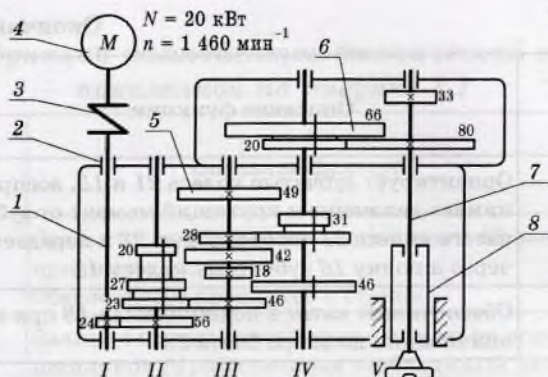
Кинематическая схема привода главного движения фрезерного станка:
